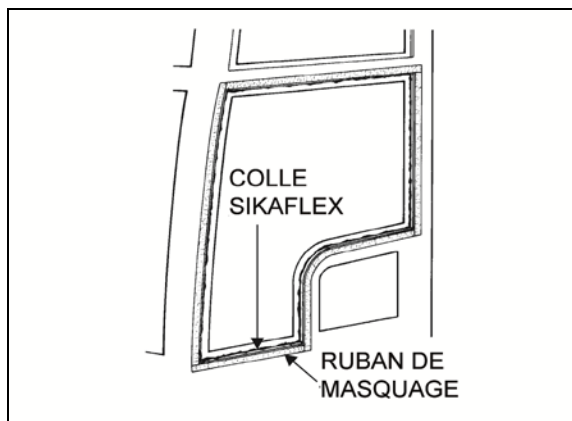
FENÊTRE FIXÉE AVEC DE LA COLLE 18081
